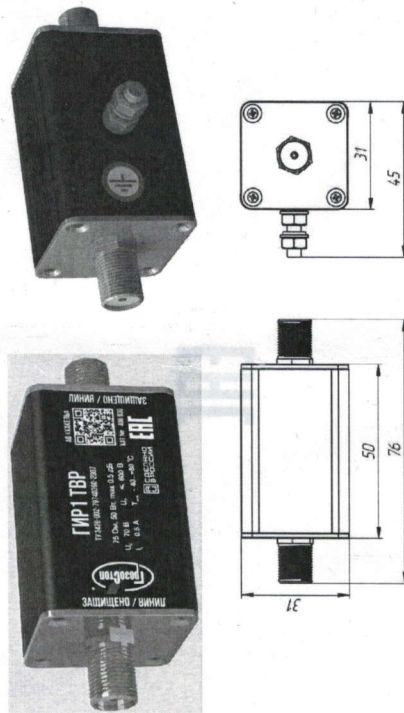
Внешний вид и габаритные размеры ГИР1 ТВР
